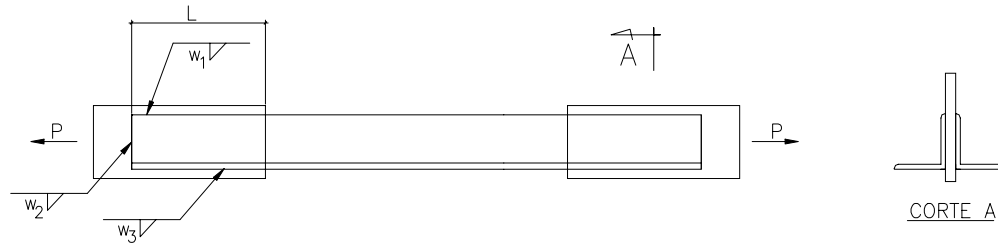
Configuração das amostras de cantoneiras soldadas para testes
